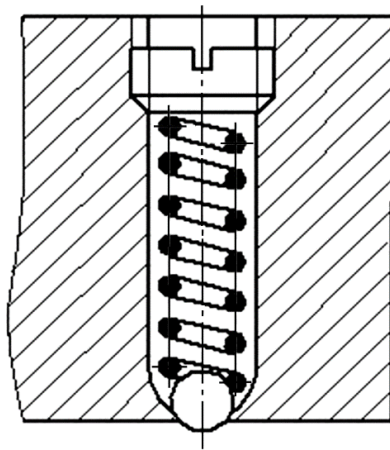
Загальний вигляд відлиплювача штампа
